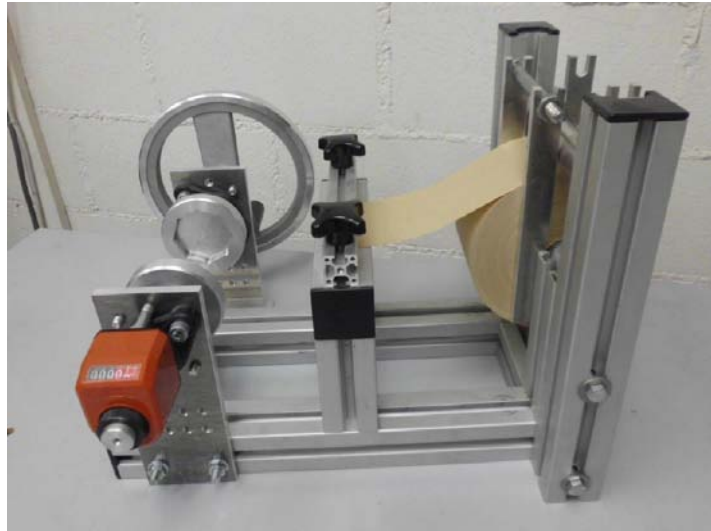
Máquina de bobinado para los objetos de ensayo.
